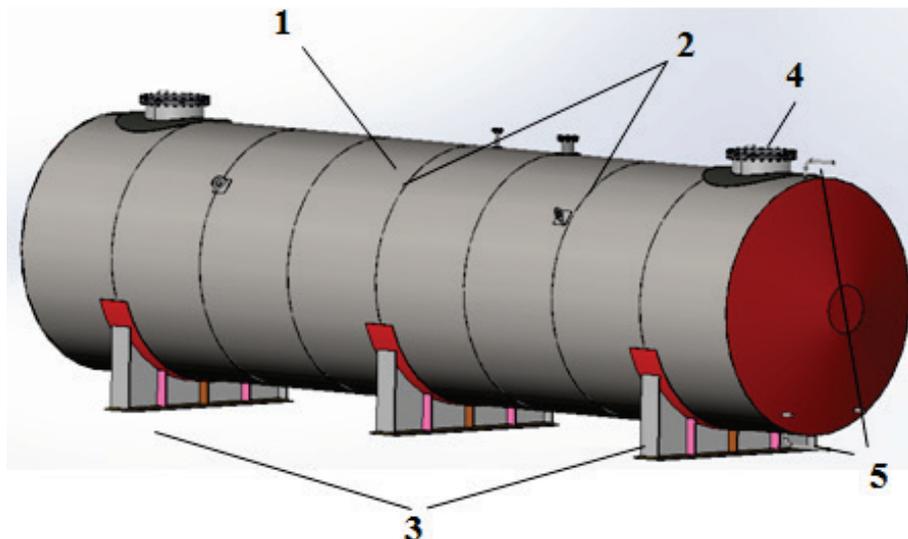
Сборка модели РГС-100: 1 — корпус; 2 — кольца жесткости; 3 — опоры; 4 — люк-лаз; 5 — патрубки входа-выхода сырья
